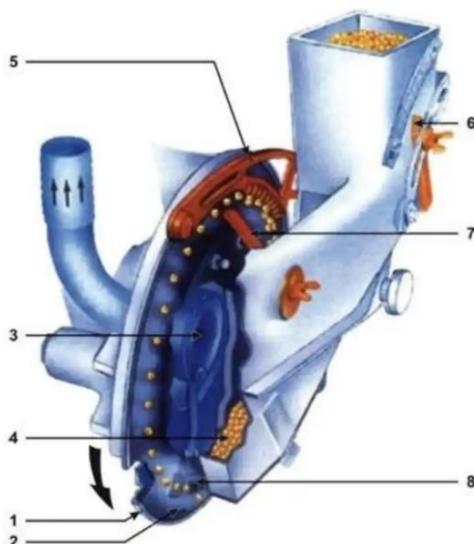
Высевающий аппарат сеялки СТВ-8: 1 – высевающий барабан; 2 - высевающий диск; 3 - полая ось, создающая вакуум; 4 – семена; 5, 7 сбрасыватели; 6- шкала; 8- прерыватель двойных семян.
